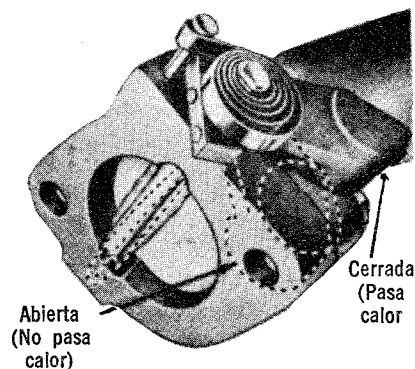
Válvula de Control de Escape. Motor 292 V-8.
